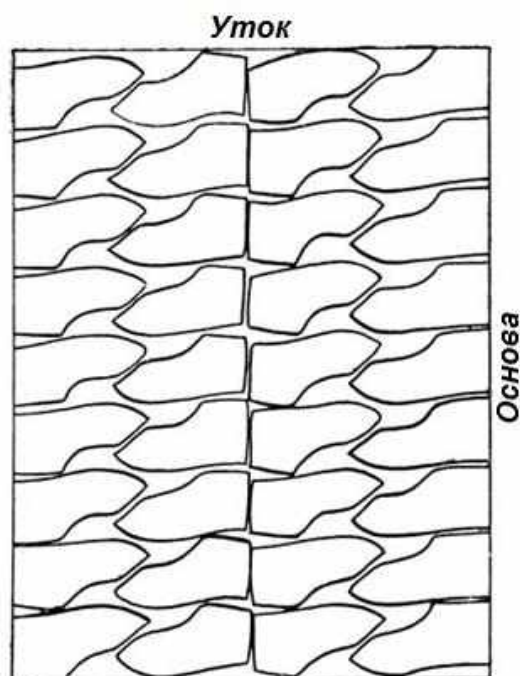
Схема раскроя многослойного настила ткани на детали подкладки
